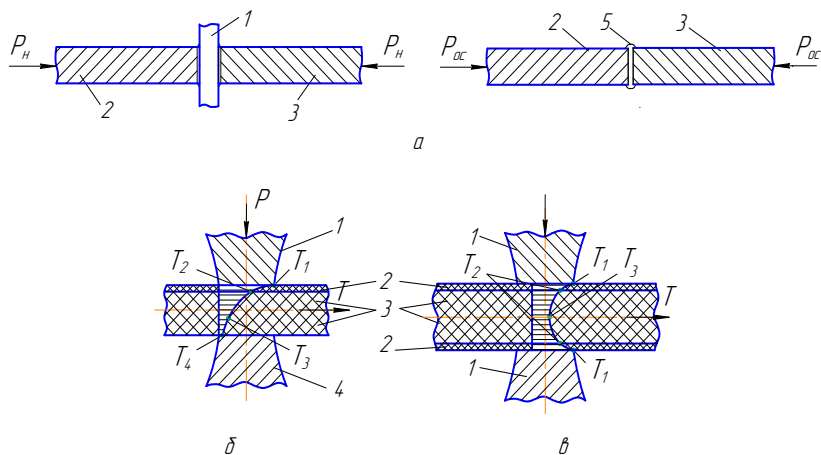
Схемы сварки нагретым инструментом: *а* — сварка прямым нагревом (*1* — нагретый инструмент; *2, 3* — свариваемые детали; *5* — сварной шов; слева — нагрев, справа — осадка); *б* — сварка нахлесточных соединений косвенным нагревом при одностороннем подводе тепловой энергии; *в* — при двустороннем подводе энергии (*1* — нагретый инструмент; *2* — разделительная прокладка; *3* — свариваемые детали; *4* — холодный инструмент;  $T_1$  и  $T_2$  — распределение температур по толщине деталей)
